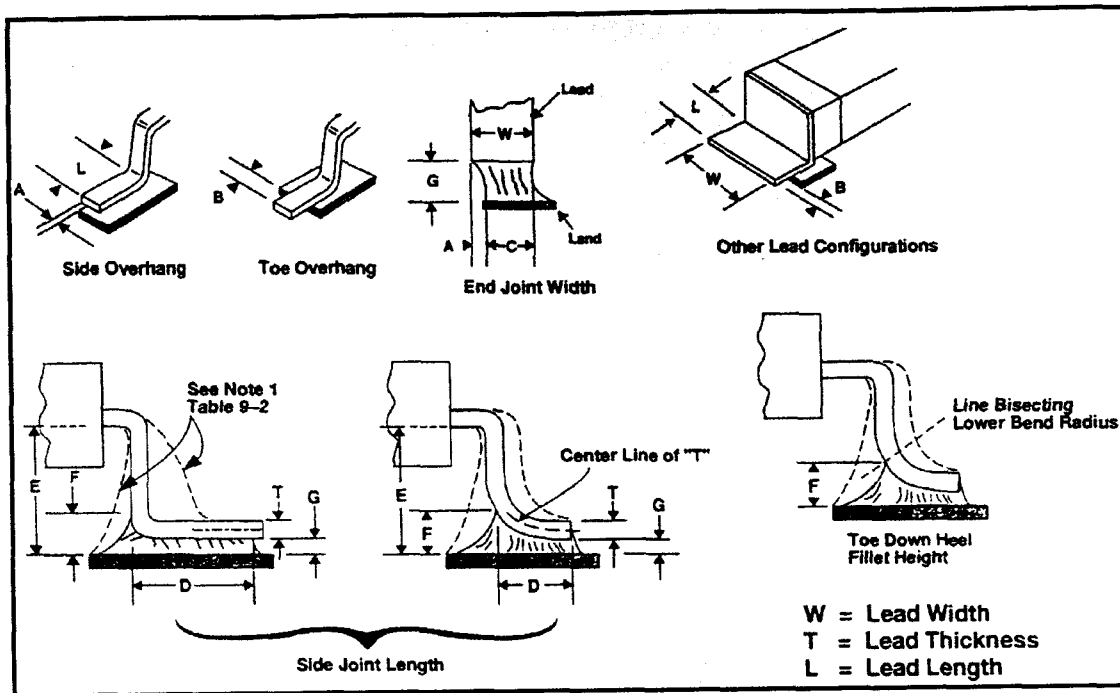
3 Criterios de dimensión para componentes SMD [1]
